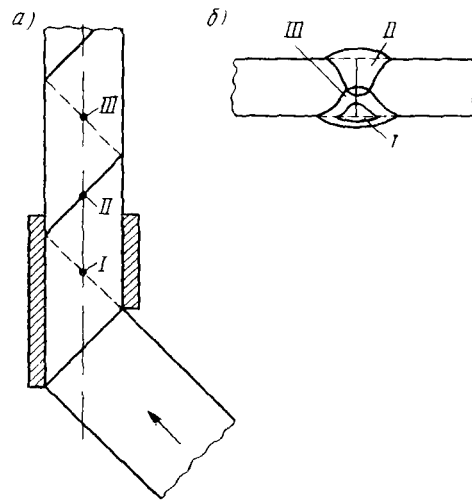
Схема сварки спирального шва трубы тремя сварочными головками:
